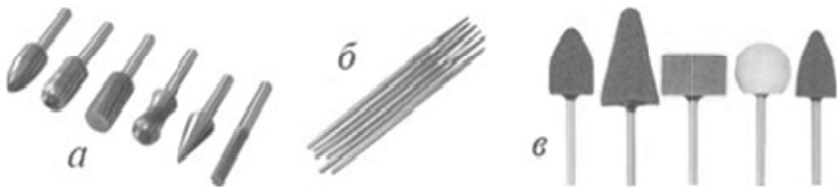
Ріжучий інструмент: а – фрези-шарошки; б – круглі напилки; в – абразивні фасонні голівки
